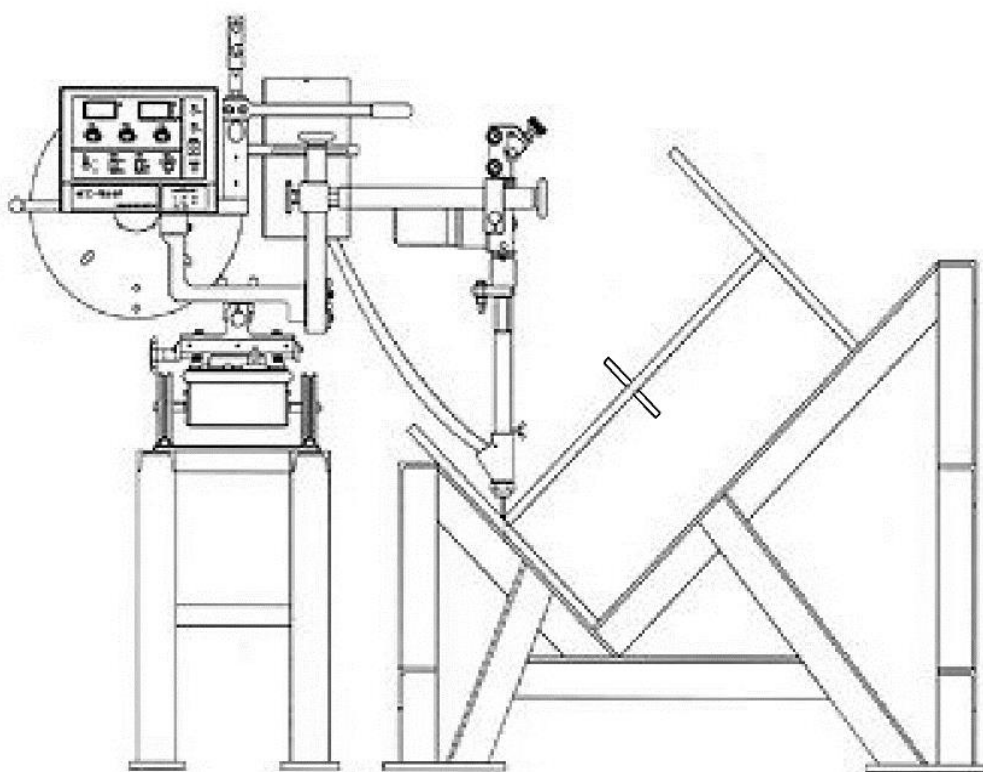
схема сварки двутавра “в лодочку”
